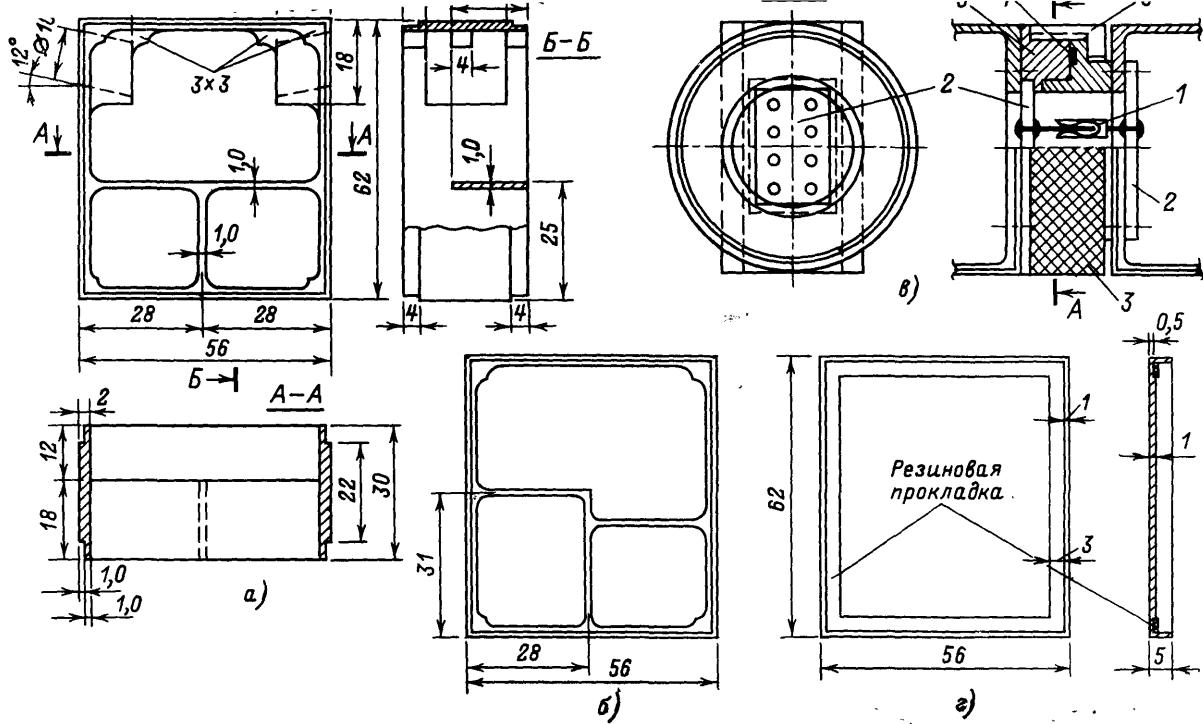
Чертежи корпусов съемных ВЧ головок (а, б), разъема (в) и крышки (г).
